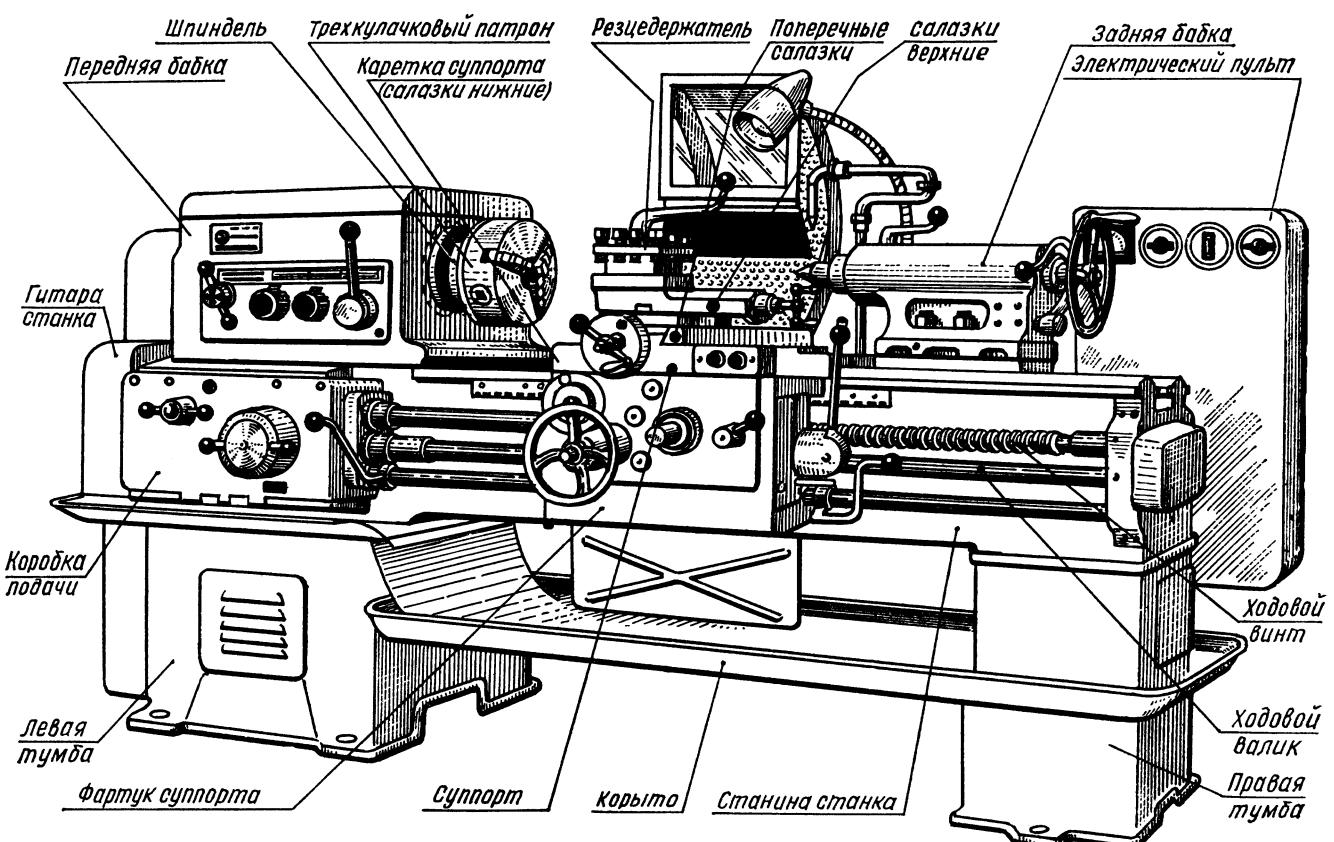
Общий вид токарно-винторезного станка 1К62
